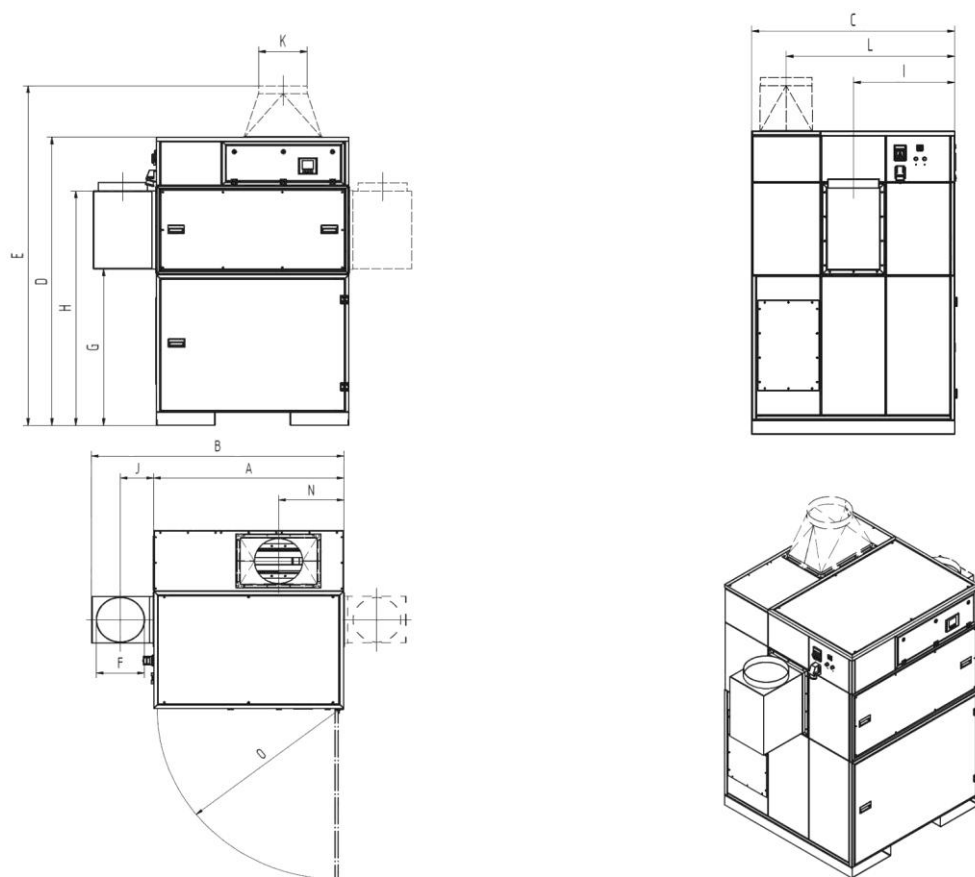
Габаритный чертеж 998701372 (998800407, 998800461)
